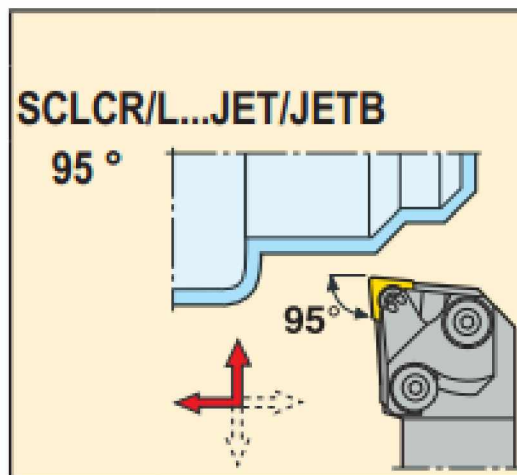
Різець для зовнішньої обробки з ромбічною пластиною CNMG
